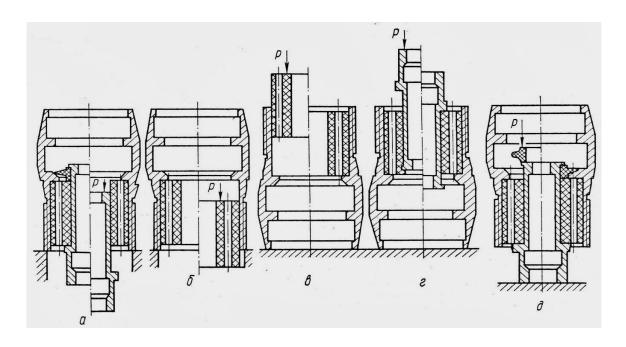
Схема выпрессовки — запрессовки деталей золотника a — выпрессовка втулки;  $\delta$  - выпрессовка амортизатора;  $\varepsilon$  — запрессовка втулки;  $\delta$  — запрессовка клапана.
